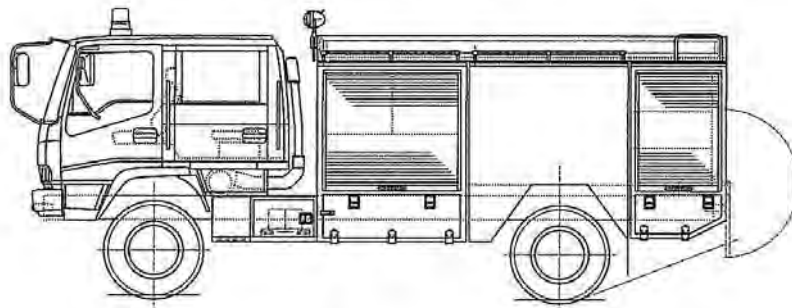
Plan de profil du fourgon pompe mousse
